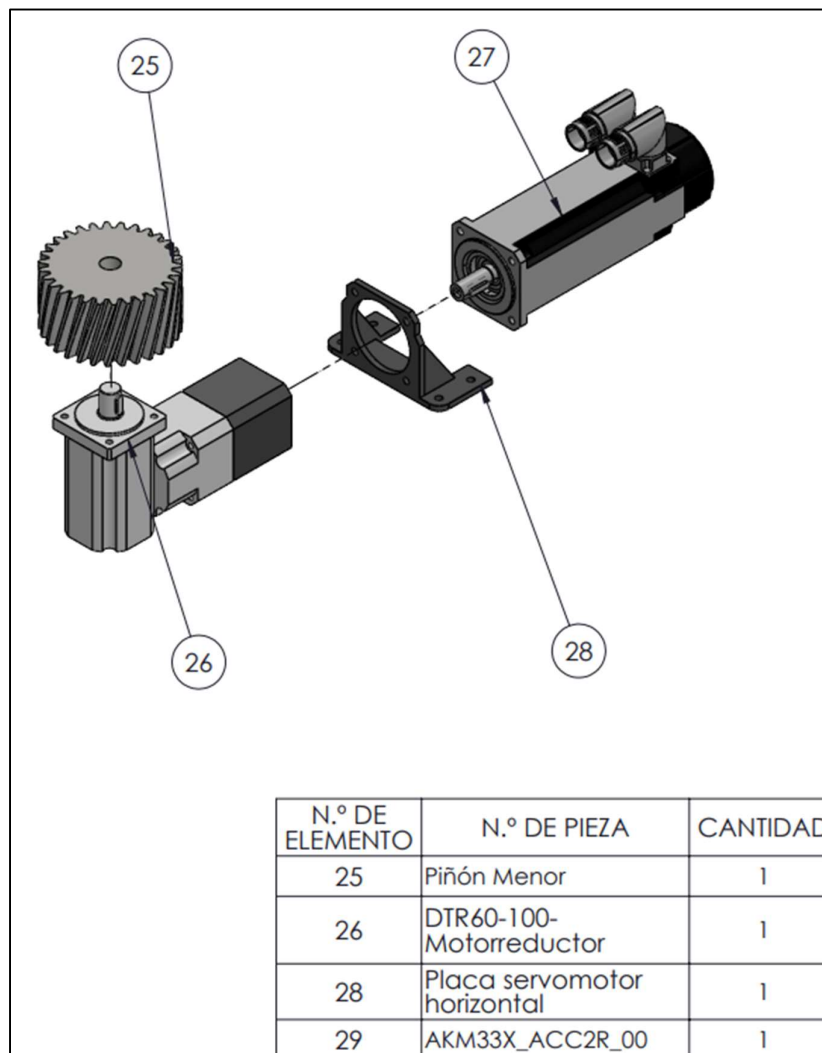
ensamble servomotor, motorreductor, placa de sujeción horizontal y piñón menor.
